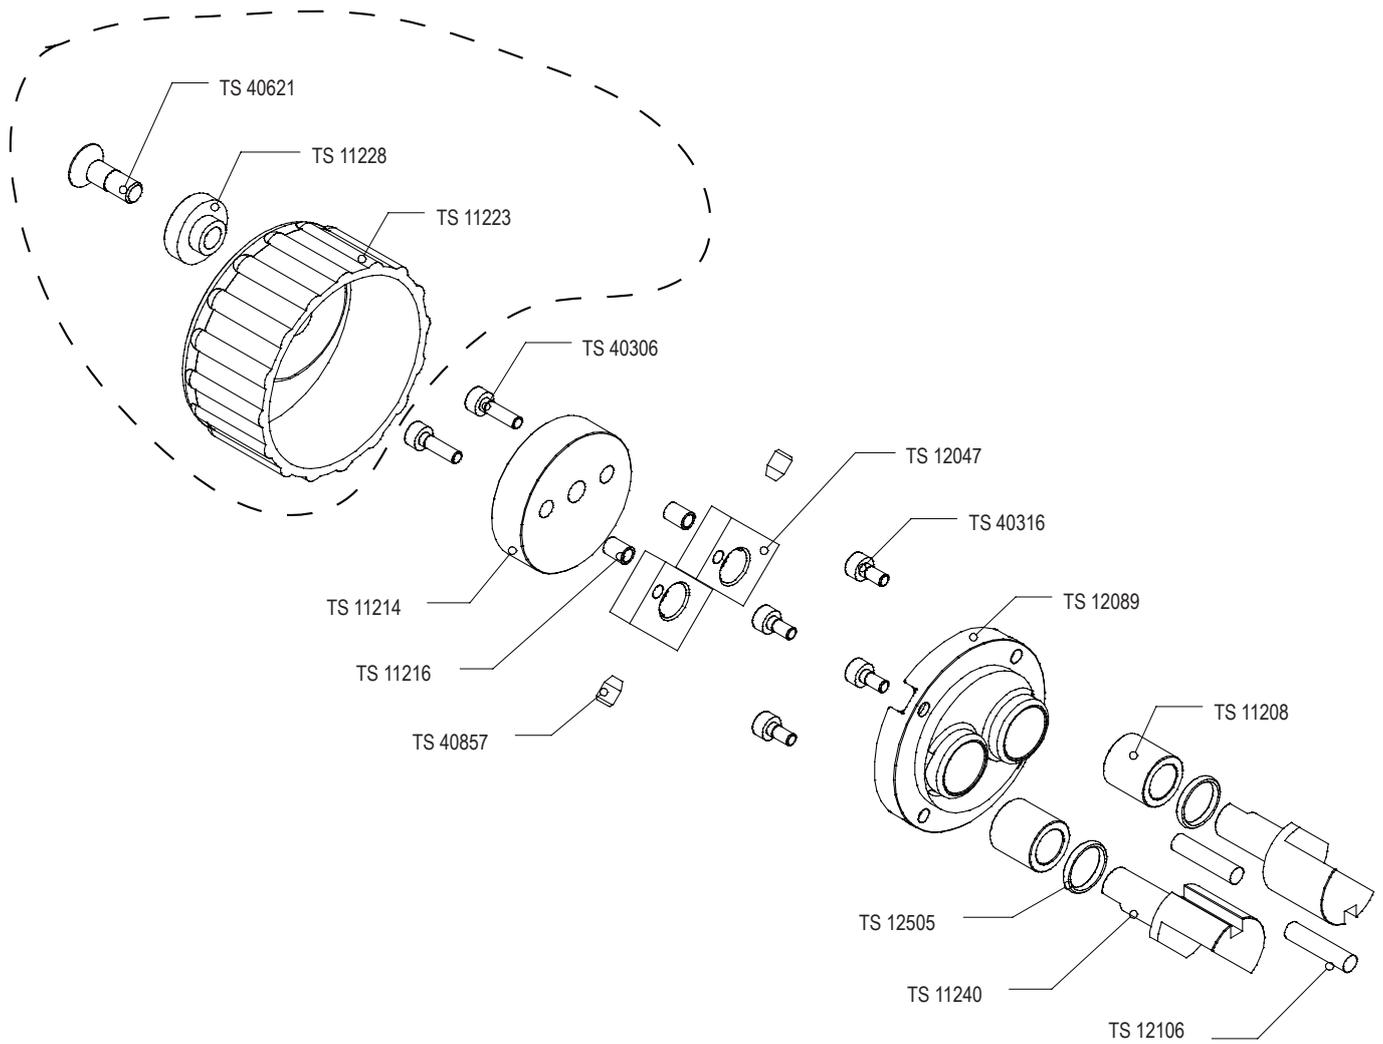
устройство очистки ленты в сборе TS 10206, детали
